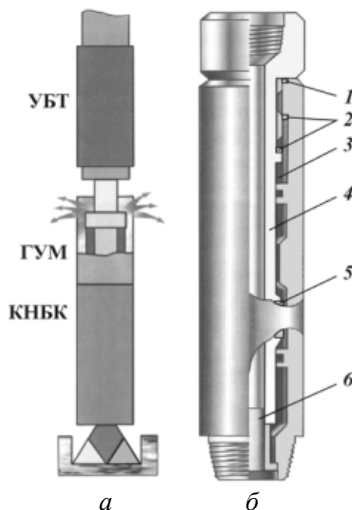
Гидравлический ударный механизм типа ГУМ и ГУМД конструкции ОАО НПО «Буровая техника»: 1, 2 – места соударения при срабатывании вверх и вниз; 3 – корпус; 4 – шпindel; 5 – дрессель; 6 – звено разрывное
